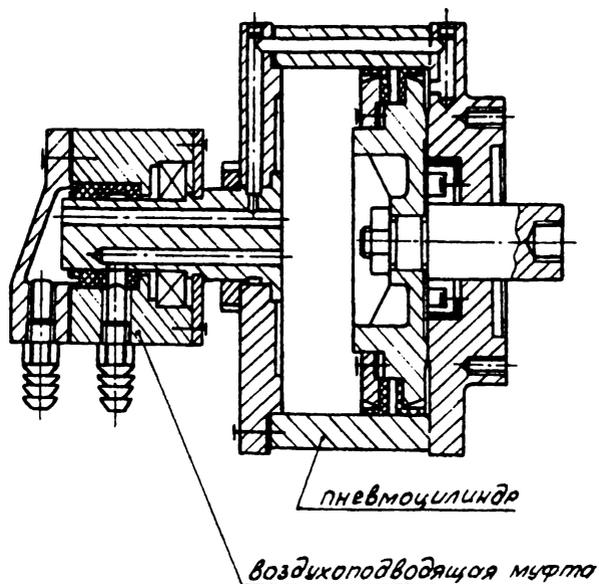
Вращающийся пневмоцилиндр с воздухоподводящей муфтой
